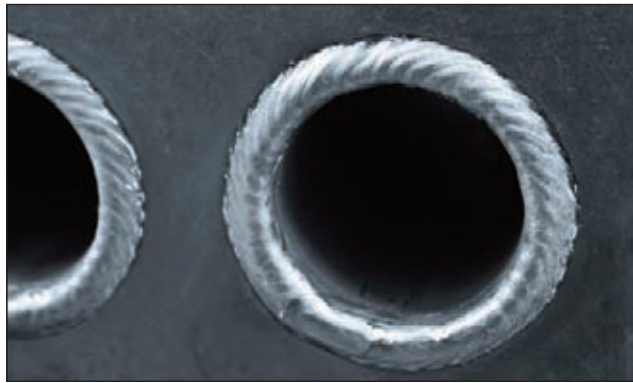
Пример сварного шва, полученного с помощью сварочной системы FTW 24-120 Pro
